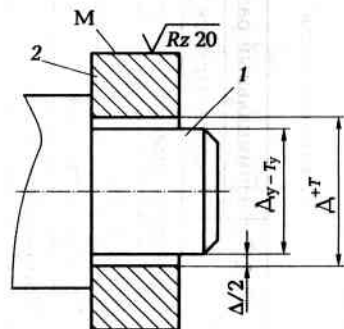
Схема установки заготовки цилиндрическим отверстием на цилиндрический установочный элемент приспособления при обтачивании наружной поверхности
